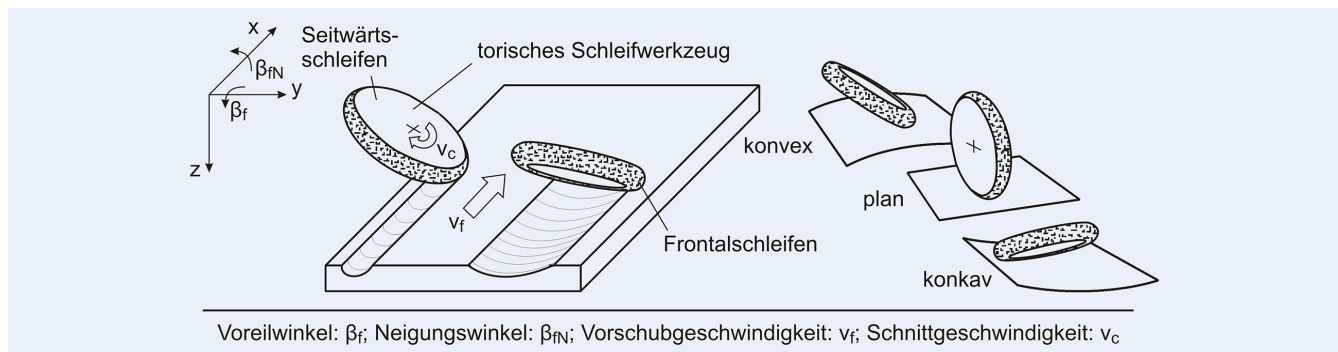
Seitwärts- und Frontalschleifen mit torischen Werkzeugen. Bild: IFW/Beh65769
